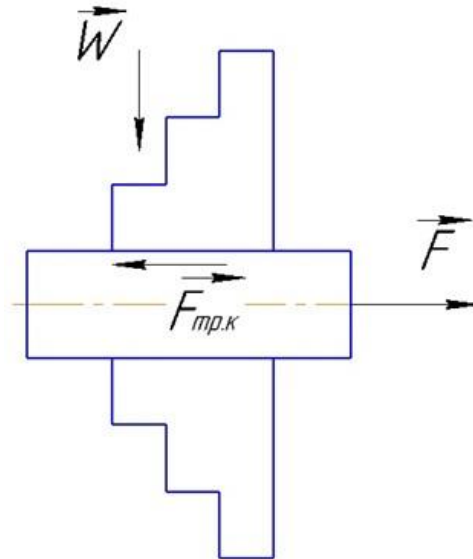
Эскиз заготовки, зажатой в кулачках вытягивателя, с расставленными на нем силами, действующими на заготовку.
